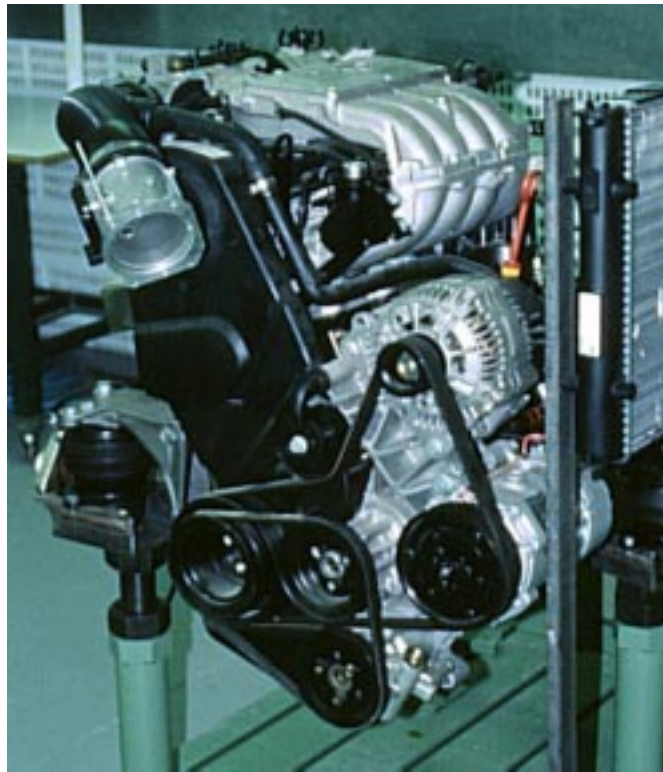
Motor SEAT AFT 1,6 I 74 kW
